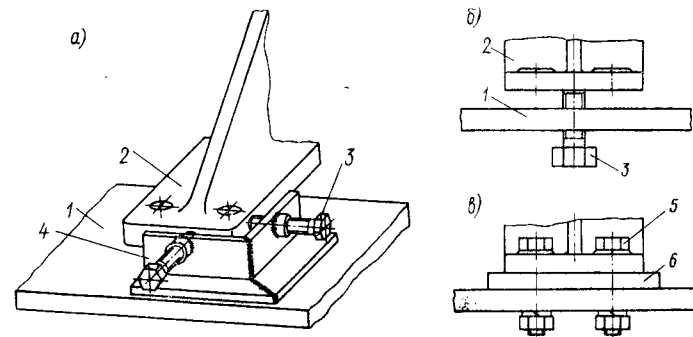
Приспособление для перемещения двигателя при центровке: а — по горизонтали; б — по вертикали; в — постановка прокладок.
